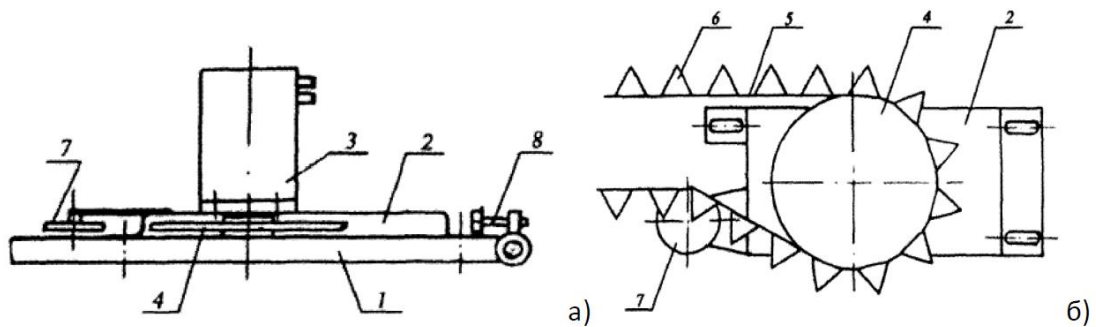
Схема привода косарки: а – вид з переду, б-вид зверху
